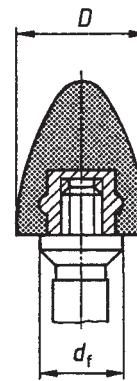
Aufspannen von Schleifkegeln Form 16, mit Gewindeinsatz
